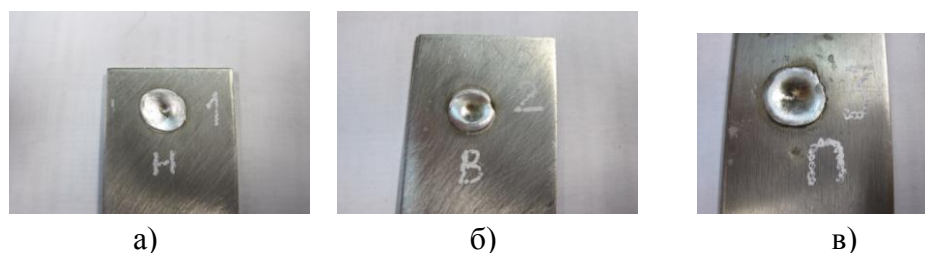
Внешний вид сварной точки в различных пространственных положениях:
